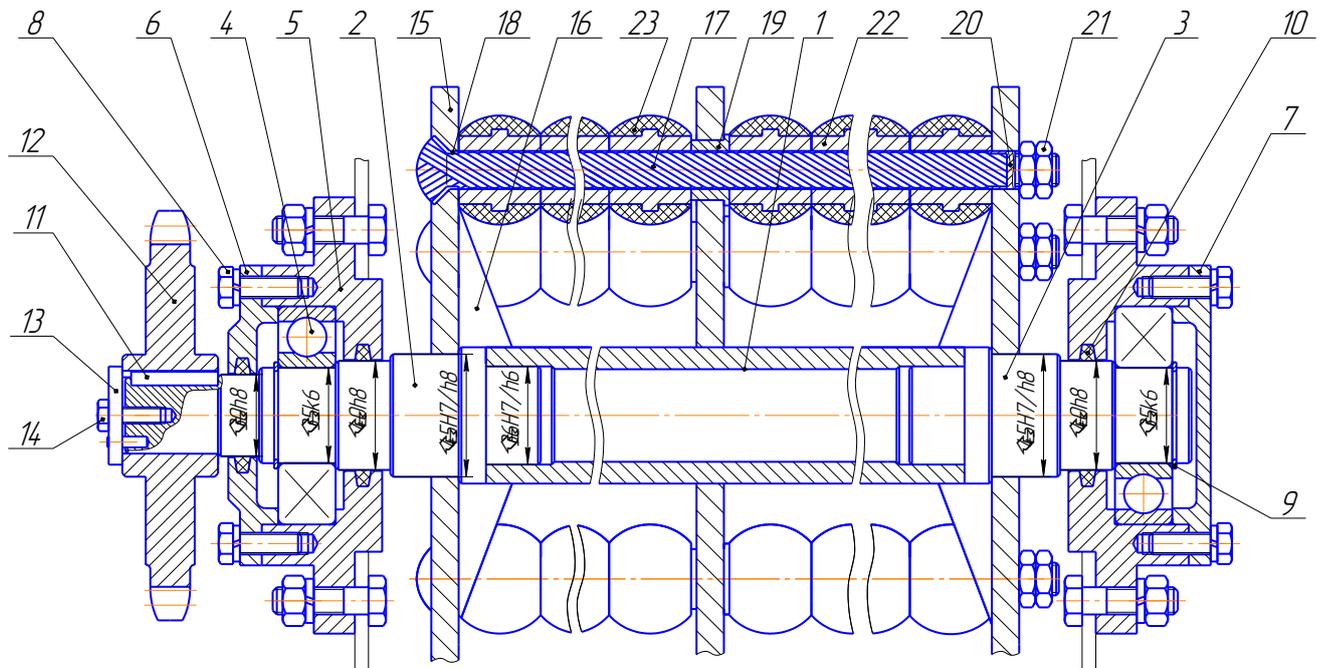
Схема битера с эластичными прутками: 1 – труба вала; 2,3 – цапфы; 4 – подшипник № 307; 5 – корпус подшипника; 6 – крышка сквозная; 7 – крышка глухая; 8 – болт М8; 9 – кольцо стопорное; 10 – уплотнение войлочное; 11 – шпонка призматическая; 12 – звездочка приводная; 13 – шайба; 14 – болт; 15 – диск; 16 – ребро жесткости; 17 – канат 12,0 ГЛ-В-Л-О-Н-180; 18 – втулка воронкообразная; 19 – втулка защитная; 20 – наконечник резьбовой; 21 – контргайка М12; 22 – втулка ударная; 23 – резиновый бандаж сферического ударника.
